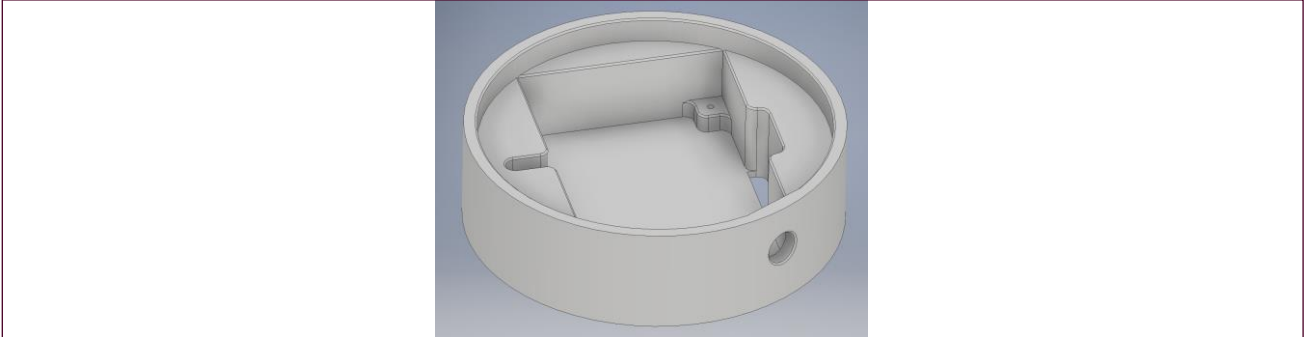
Zeichnung des Gehäuses für die Printplatte
